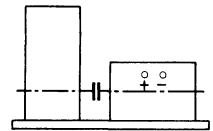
Benzin- oder Dieselmotor gekuppelt mit Schweißmaschine.
